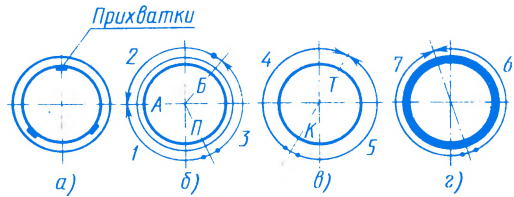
Порядок сварки стыков неповоротных труб:
